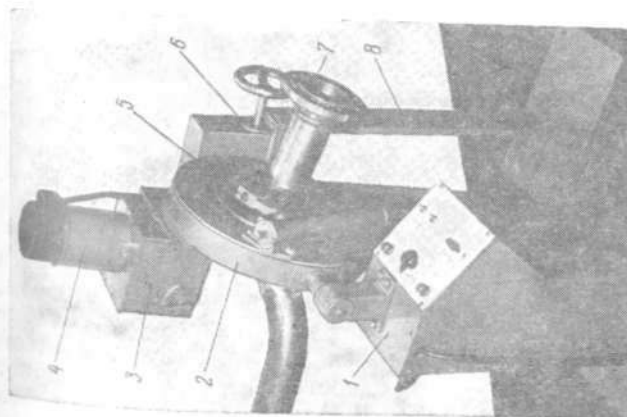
Манипулятор для сварки кольцевых швов.
